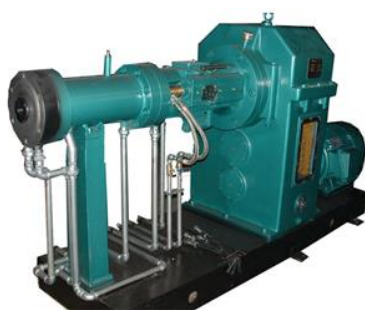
เครื่องจักรแม่พิมพ์แบบฉีด (injection molding machine) (สถาบันพลาสติก, 2013)
